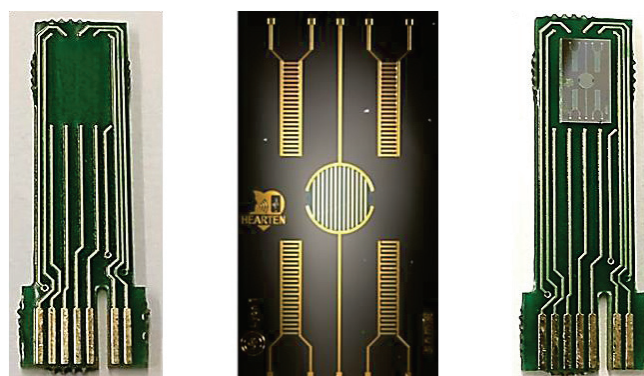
Photo de la µIDE et de son PCB avant et après collage
